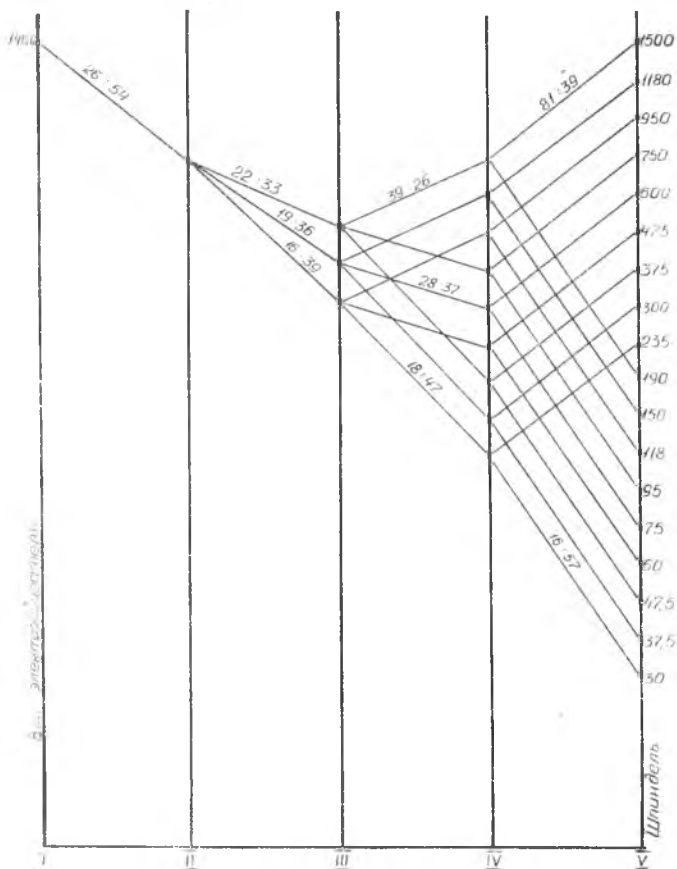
Картина чисел оборотов коробки скоростей станка 6Н83Ш
